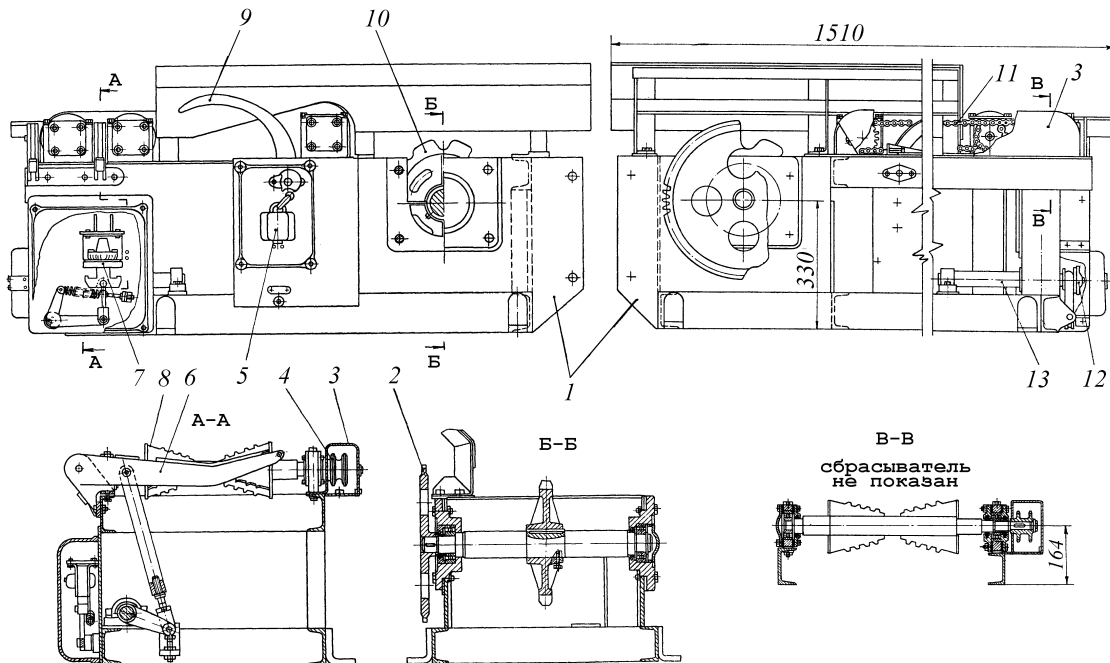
Головная часть подающего транспортера: 1 – рама; 2 – звездочка; 3 – ограждение цепной передачи; 4 – двойная звездочка привода роликов; 5 – конечный выключатель ВК-211; 6 – сбрасыватель остатка; 7 – электромагнит; 8 – ролик; 9 – флажок; 10 – ведущая звездочка транспортера; 11 – цепь привода роликов; 12 – муфта включения сбрасывателя остатка; 13 – вал сбрасывателя остатка
